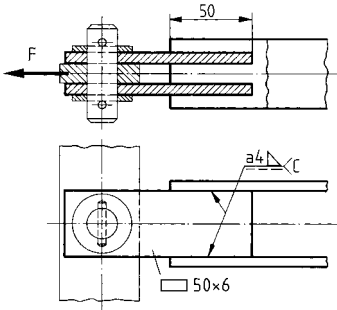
Geschweißter Gabelkopf einer Zugstange
